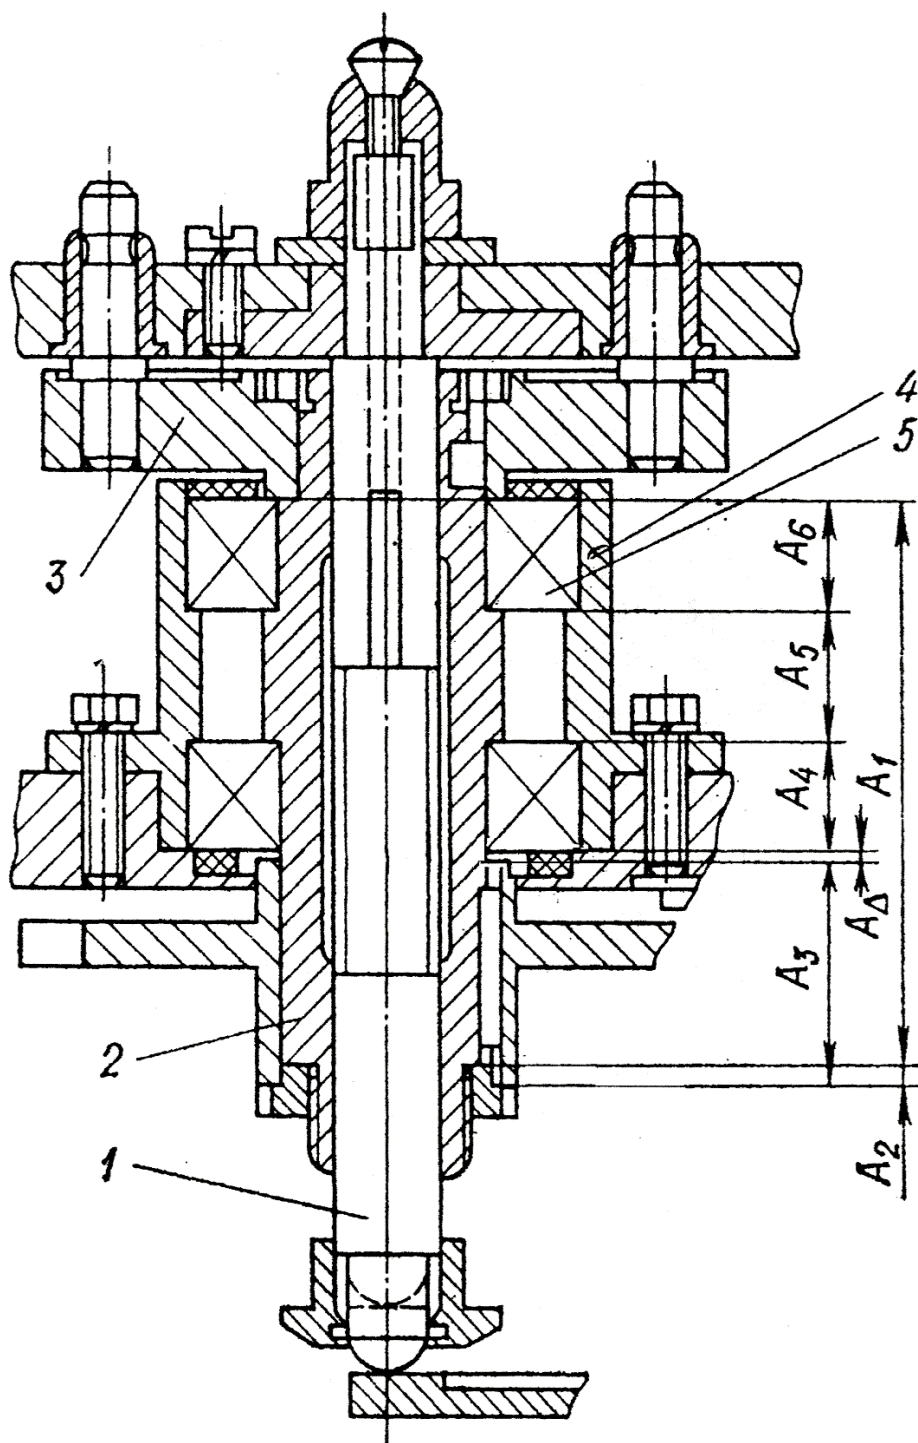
Узел подшипникового соединения: 1 – ось; 2 – вал; 3- диск;
